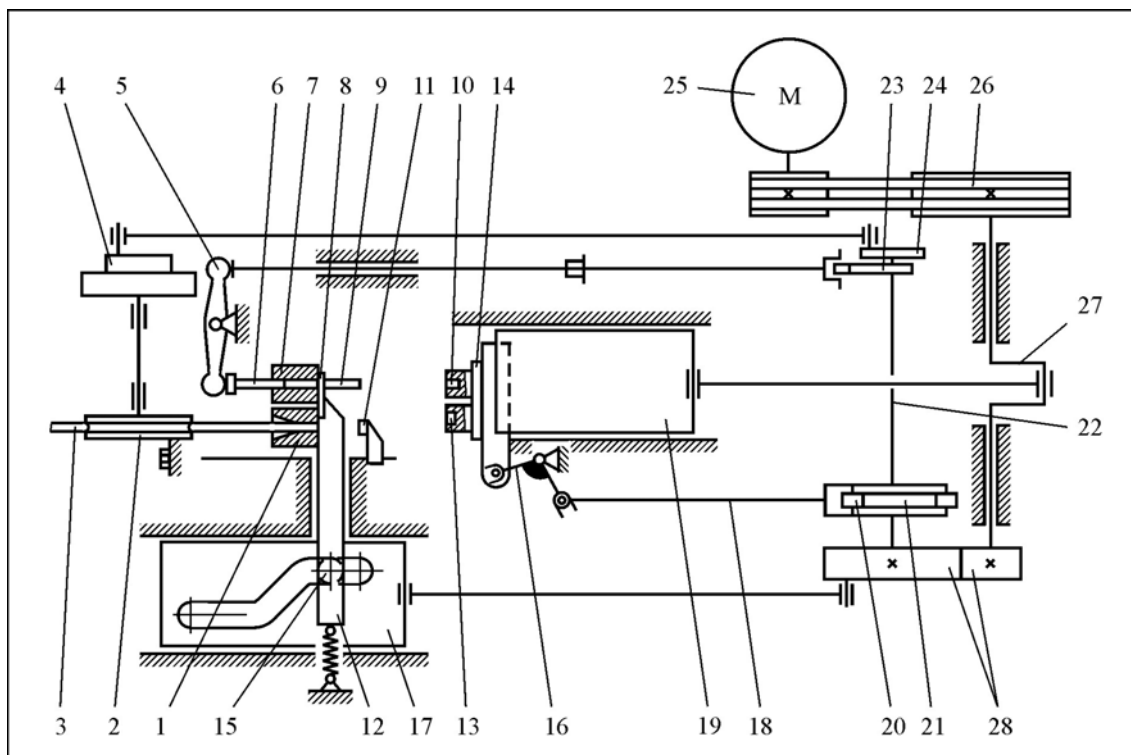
Кінематична схема двоударного однопозиційного автомата А1221: 1 – відрізна матриця; 2- ролики; 3 – заготовка-дріт; 4 – храповий пристрій; 5 – важіль; 6 – виштовхувач; 7 – висаджувальна матриця; 8 – ніж; 9 – заготовка; 10 – пуансон; 11 – упор; 12 – ножовий шток; 13 – пуансон; 14 – ползок; 15 – ролик; 16 – двоплечий важіль; 17 – бічний повзун; 18 – шатун; 19 – головний повзун; 20 – ролик; 21 – кулачковий механізм; 22 – розподільний вал; 23 – виштовхувач; 24 – диск; 25 – електродвигун; 26 – клинорімінна передача; 27 – колінчастий вал; 28 – зубчаста передача
